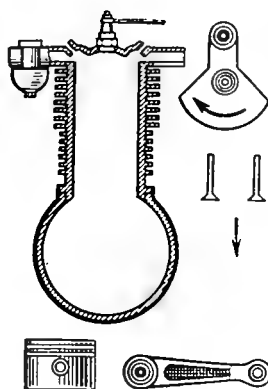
Мультипликационные заготовки для съёмки технического сюжета: а — собранная заготовка; б — элементы заготовки.
